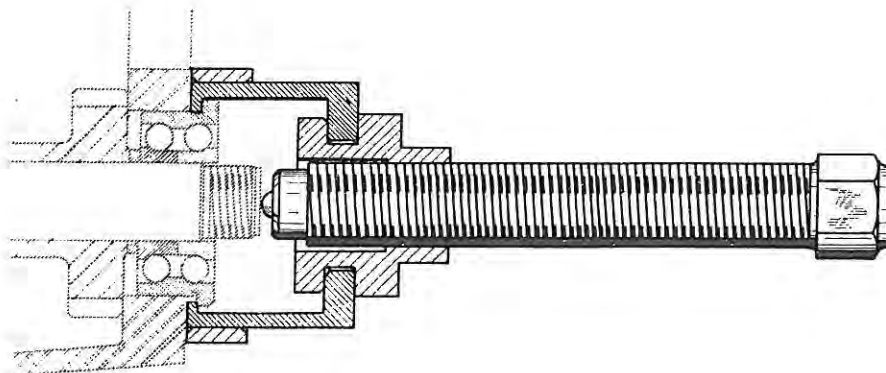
Schlüssel f. Schraube am Gabelbolzen erhältl. unter 1705-T
